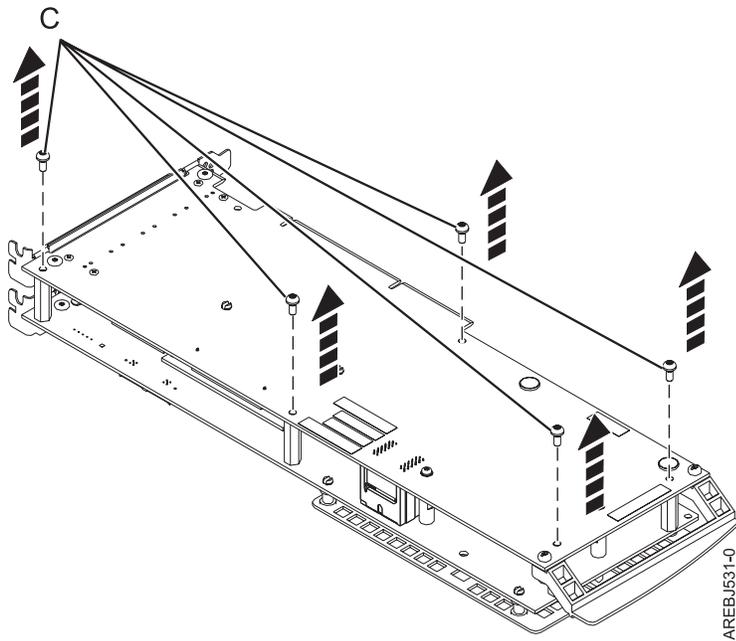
Position der Schrauben auf dem Kartengruppenadapter 572F/575C
